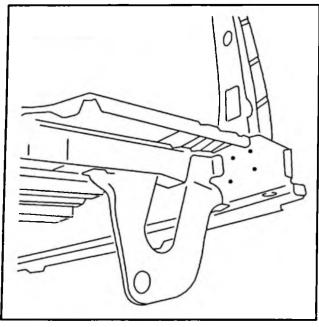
CP0DSC Souder par points électriques. Souder par points bouchons MAG.
